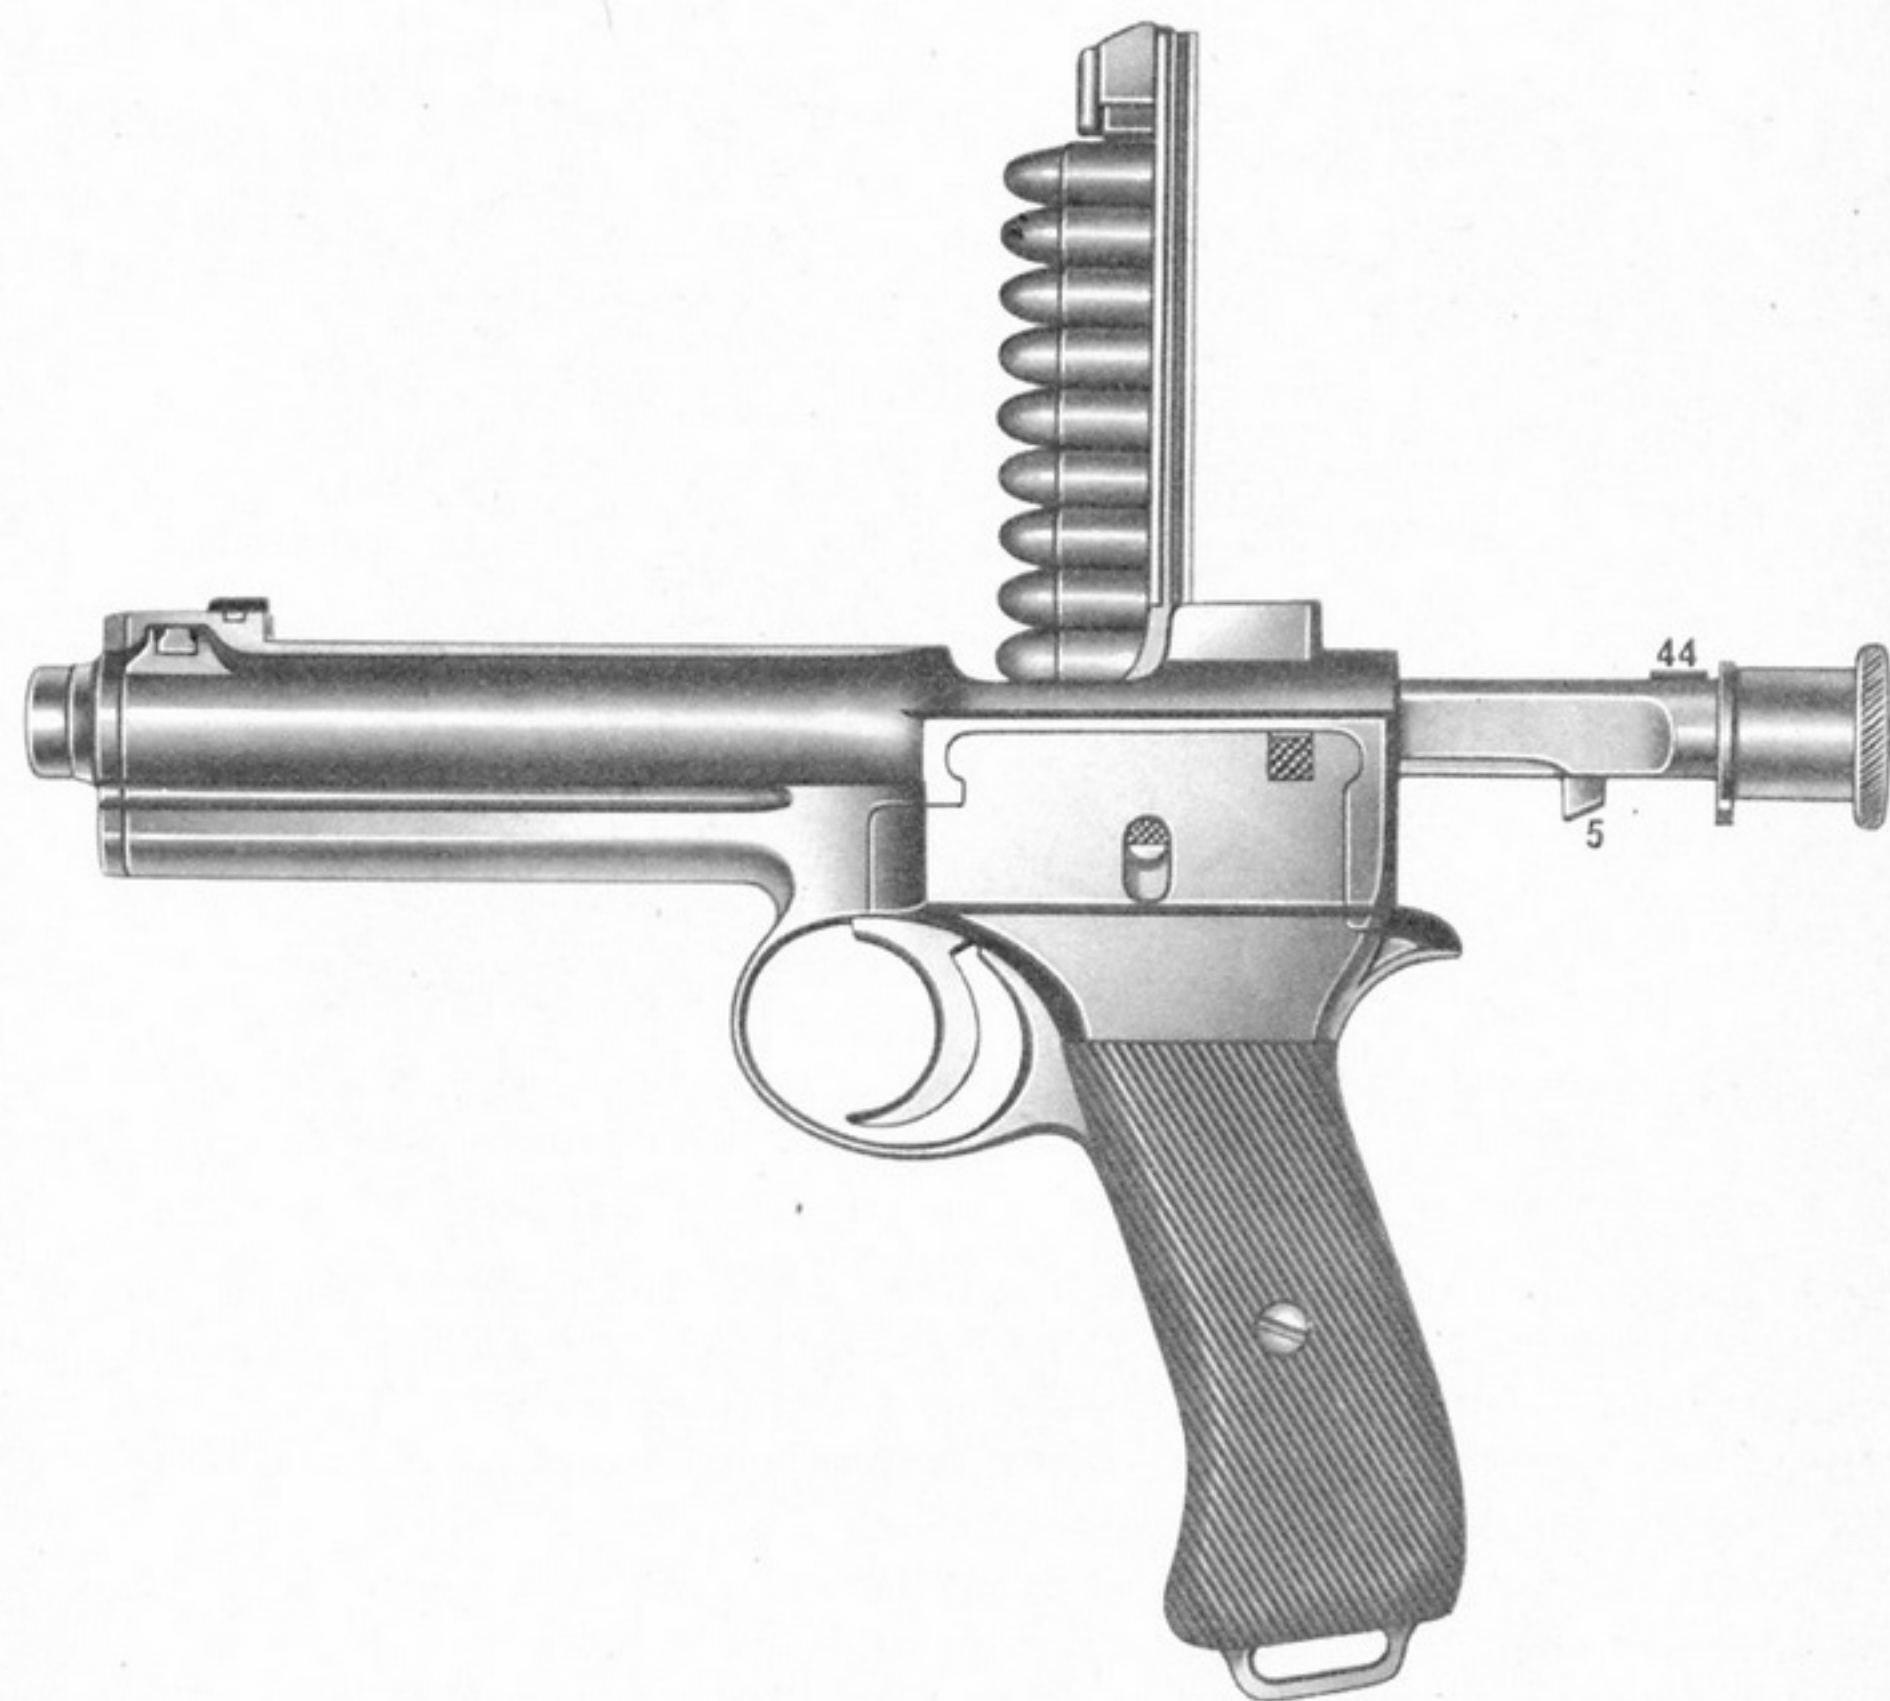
Roth-Steyr, M 1907, mit Ladestreifen (5 = Schlagbolzenrast, 44 = Drehsicherung) Pistole im Ruhestand:
